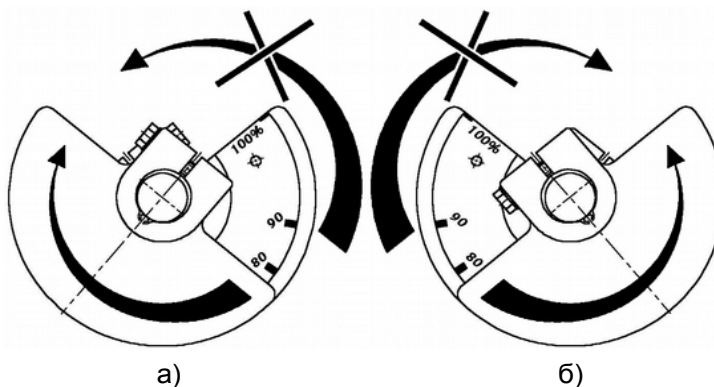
А. Схема регулировки статического момента плавно регулируемых дебалансов:
